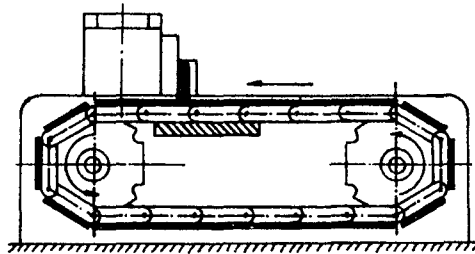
Princíp práce reťazovej pret'ahovačky
